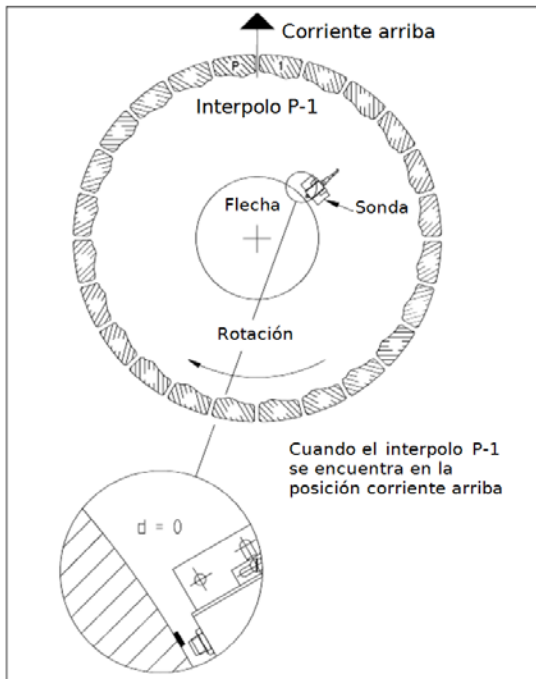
Posición de P-1 en el rotor dando frente a la corriente arriba.
